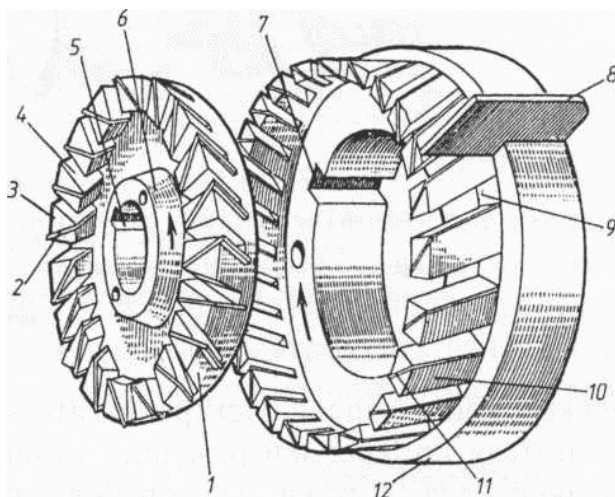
Рабочие органы режущего механизма эмульсатора «Карл Шнель»:
